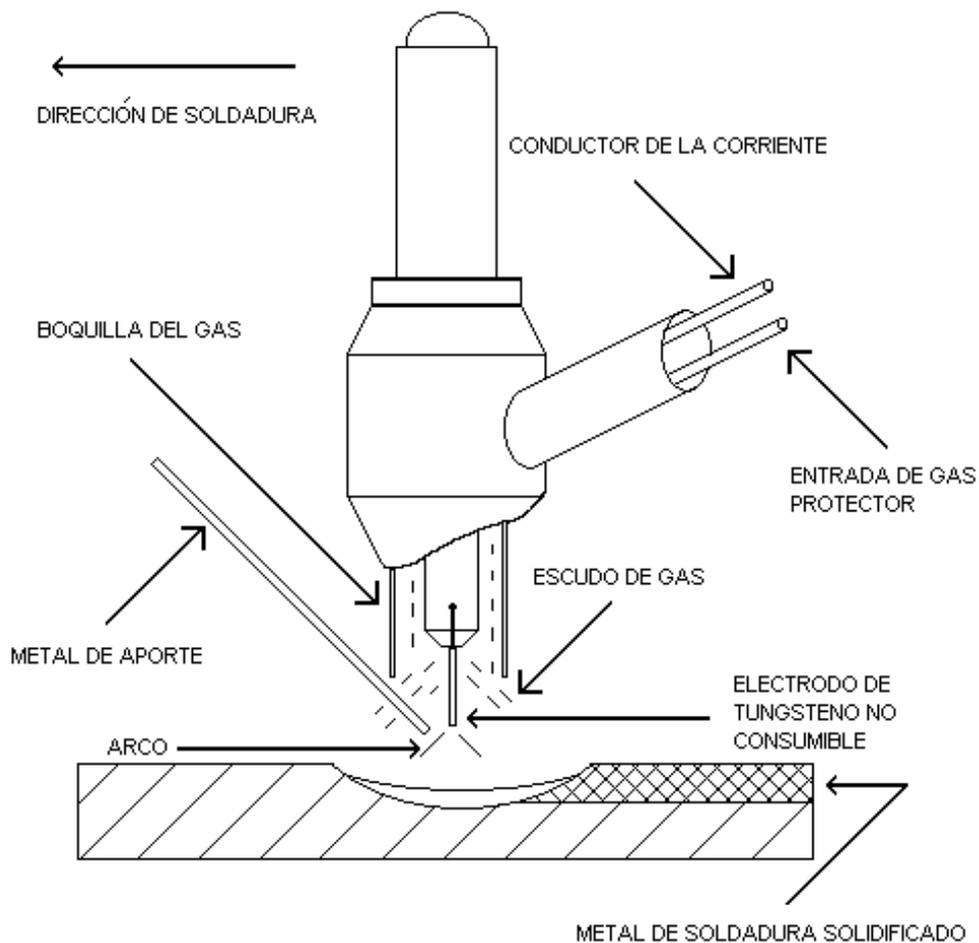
Operaciones de soldadura por arco de tungsteno y gas
